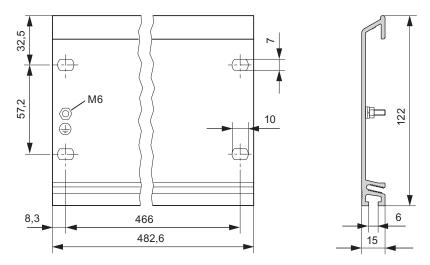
Plan d'encombrement du profilé support de longueur standard 482,6 mm
